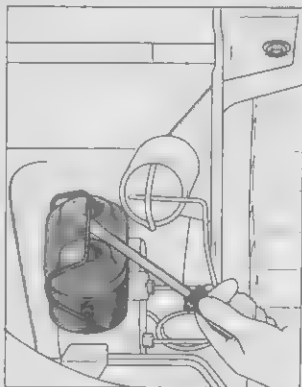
13. Снятие с помощью отвертки крышки металлического главного цилиндра
